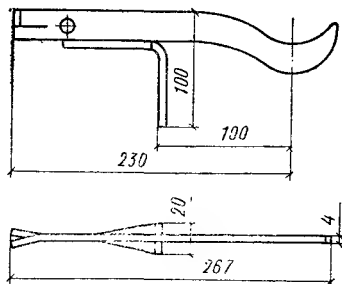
Кронштейн типа 3кс (масса 0,258 кг) для крепления радиаторов на пенобетонных стенах с заделкой цементным раствором
